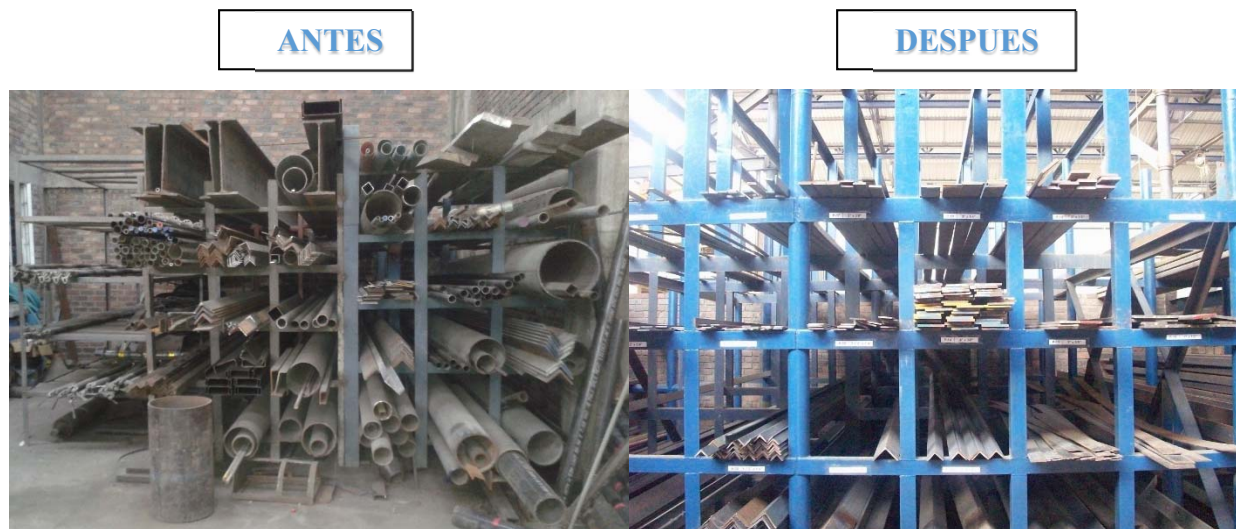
Cambio de estanterías (Fuente: Elaboración propia)
